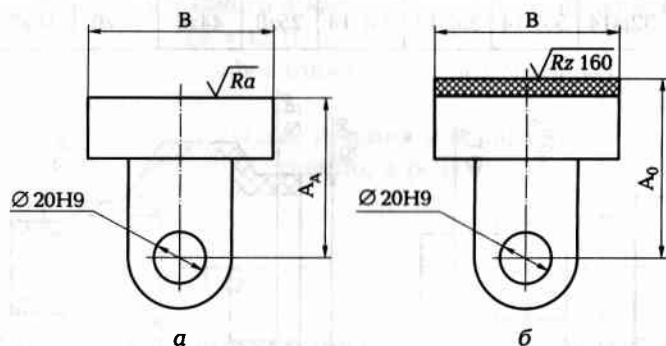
Схема обработки плоской поверхности: а — размеры детали; б — размеры заготовки
